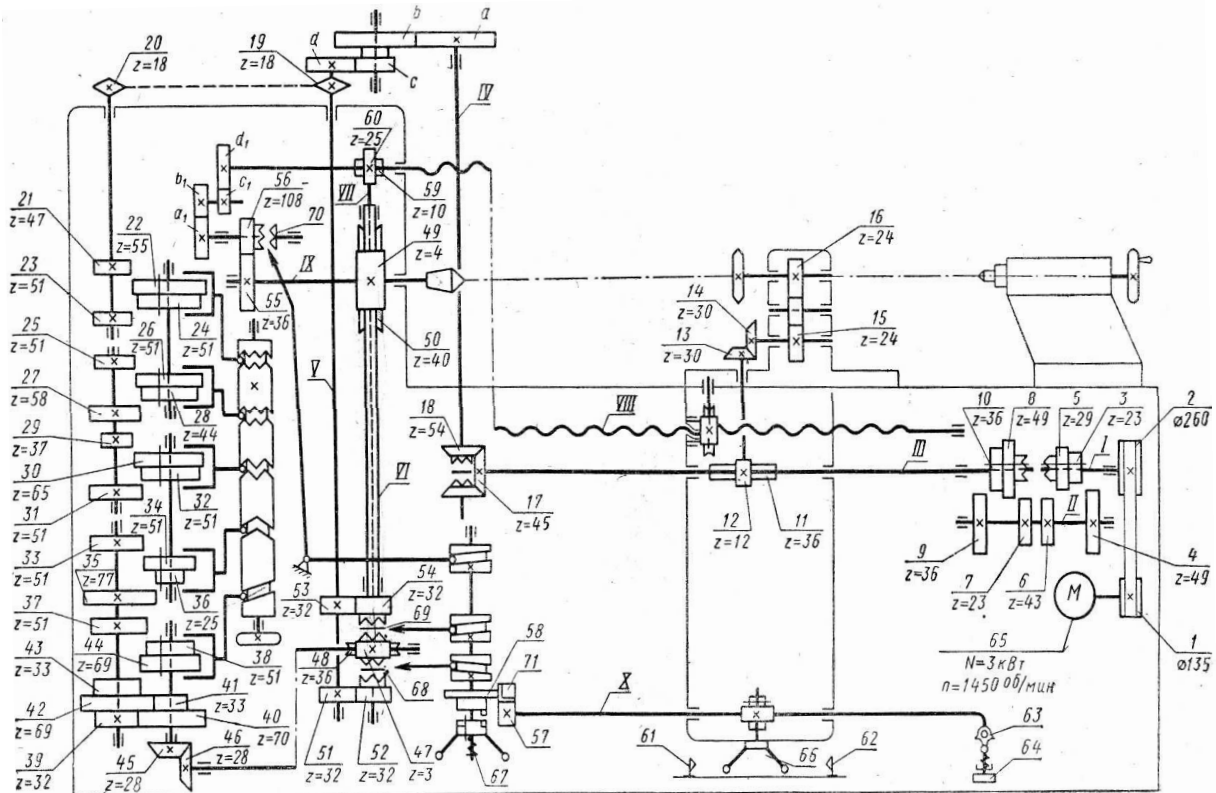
Кинематическая схема резьбофрезерного станка для обработки длинных резьб
